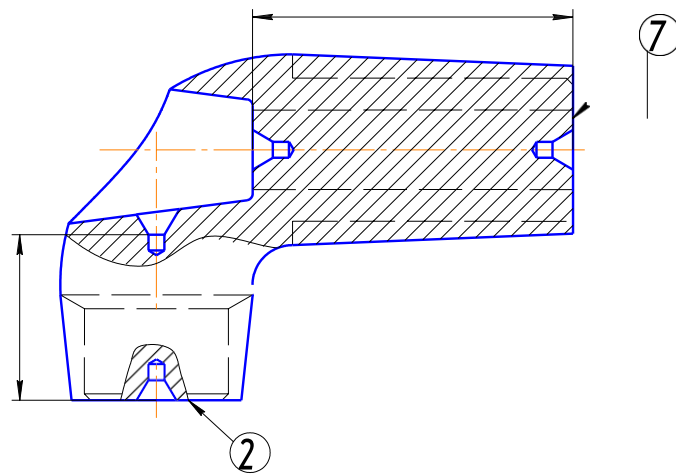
Фрезерно-центрувальна операція (операційний ескіз)
